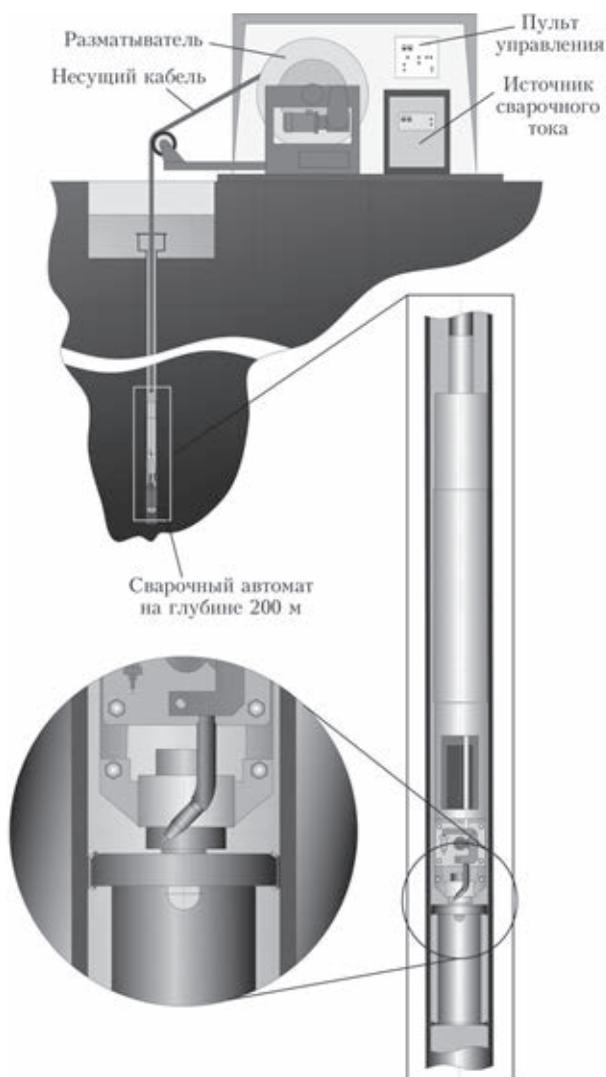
Комплекс оборудования для автоматической сварки на большой глубине внутри трубы
